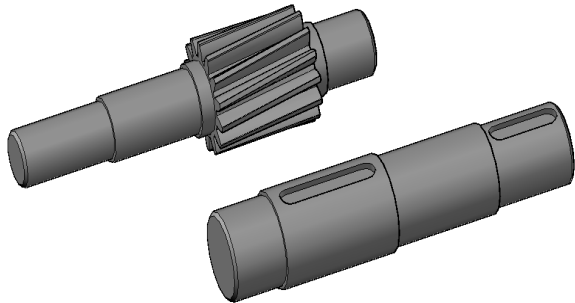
Вали редуктора з фасками та пазами для шпонки
